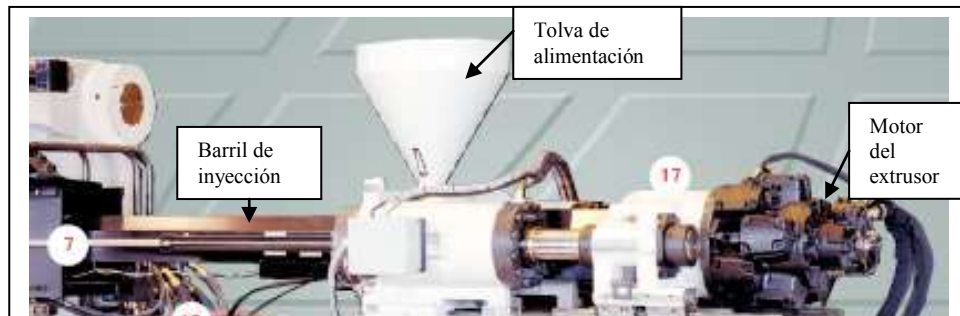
Partes principales de la unidad de inyección. (partes expuestas).
